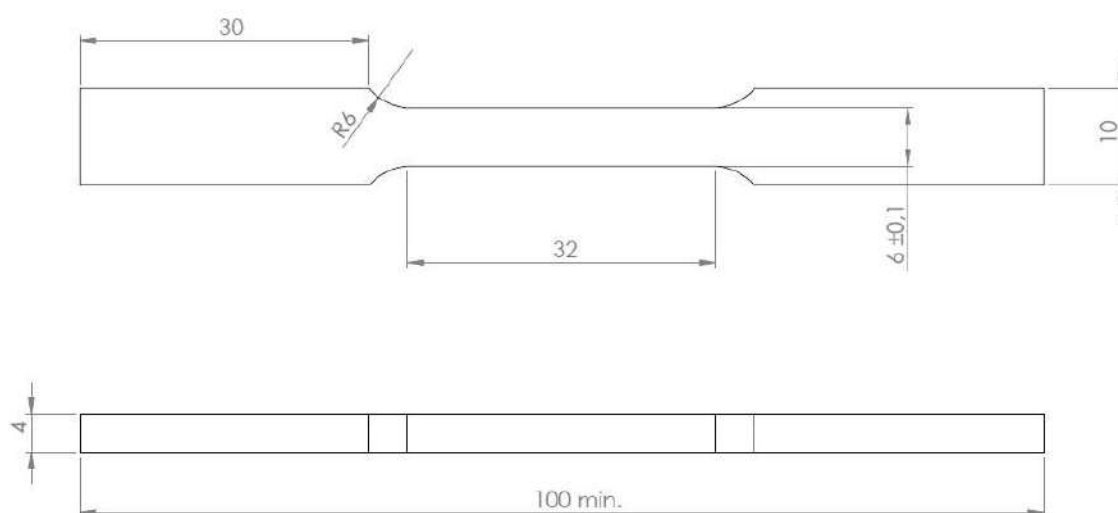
Dimensões (mm) dos corpos de prova de tração (ASTM B557-15).
